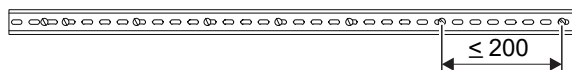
Fixation du rail de montage (spécifications en mm)
